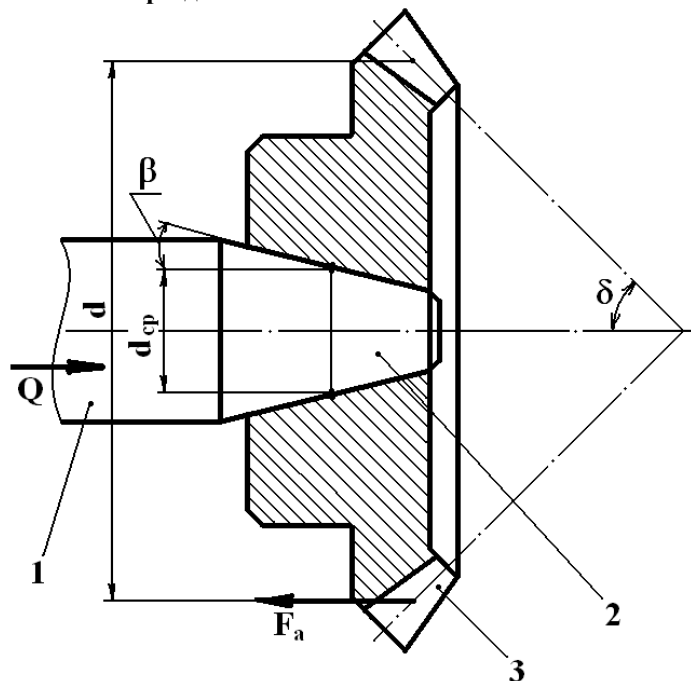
Безшпонкове з'єднання конічного зубчастого колеса з валом
